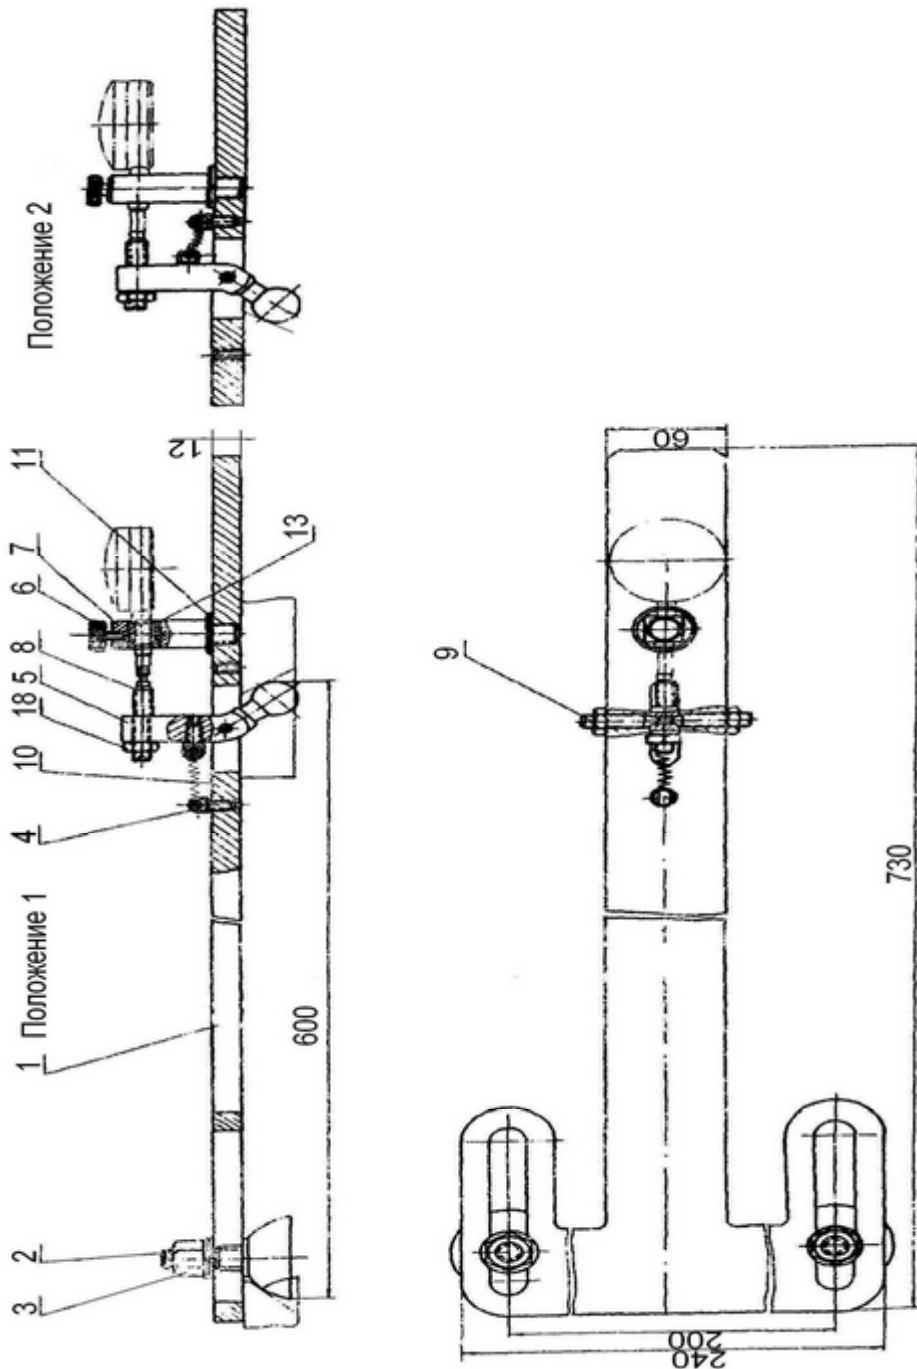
Приспособление для проверки параллельности направляющих типа «ласточкин хвост» СД 8532 – 4013
